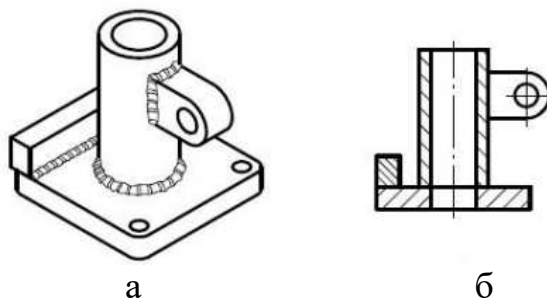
З'єднання деталей за допомогою зварювання
